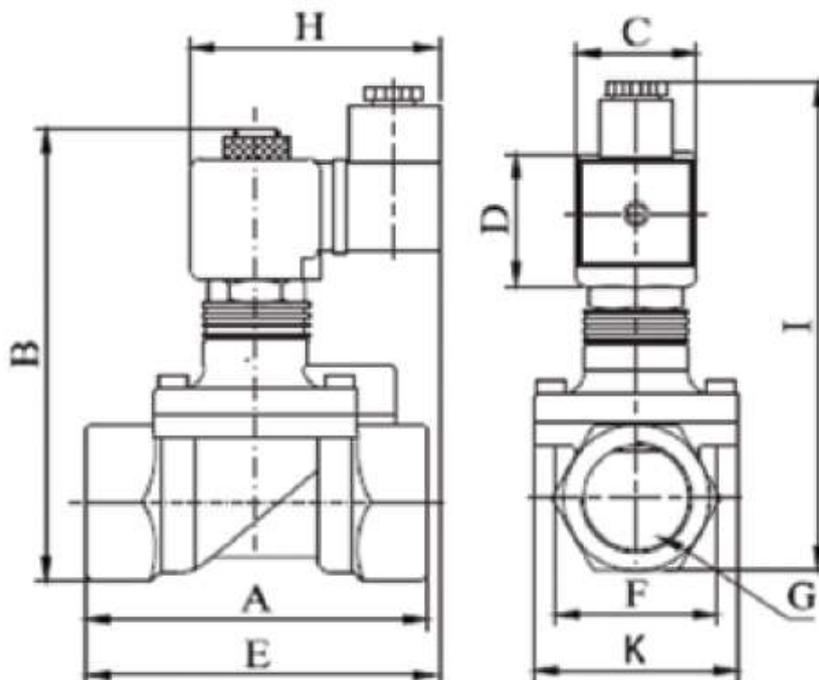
Габаритные и присоединительные размеры клапана типа EV225R
